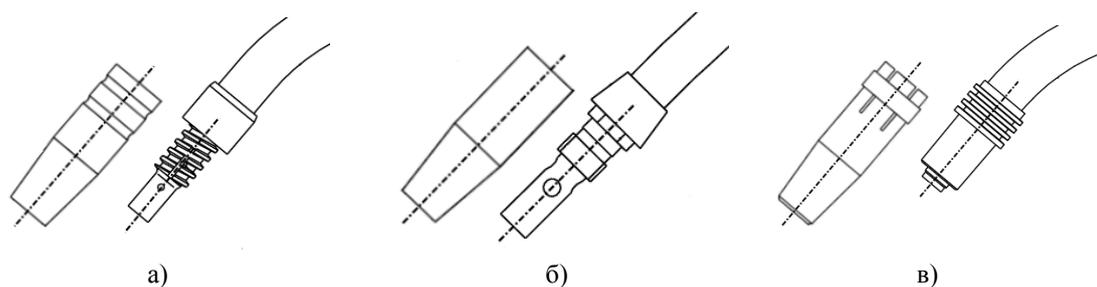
Конструкции крепления сопел к сварочным горелкам
